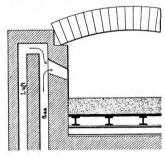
Gasrohrschweißofen mit Generatorfeuerung.
